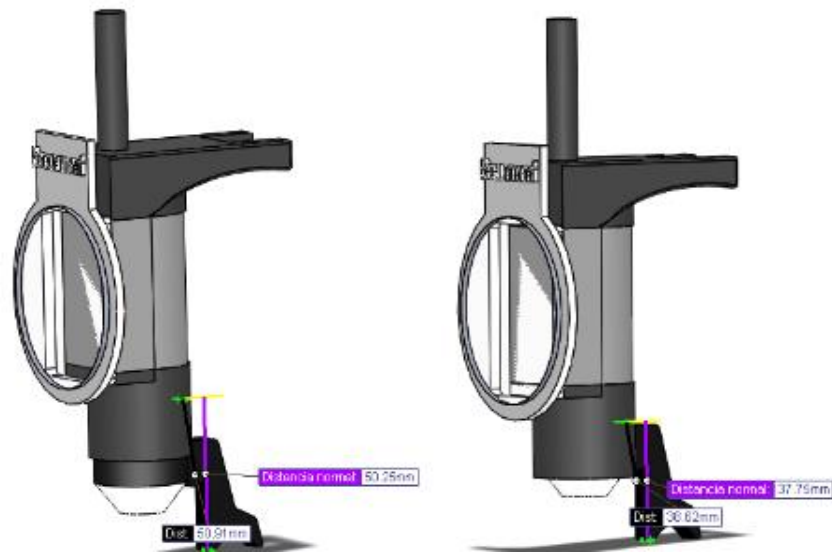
Posición inicial dispensador (Izq.), posición final dispensador (Der.)
